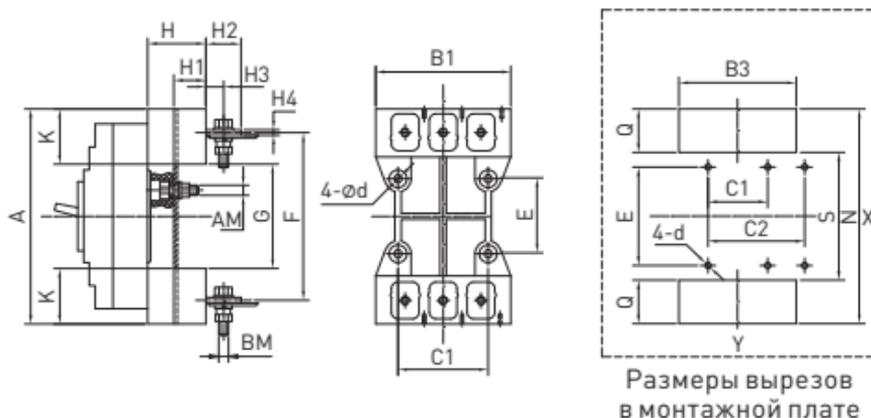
Габаритные и установочные размеры втычной панели ВА-99М заднего присоединения
